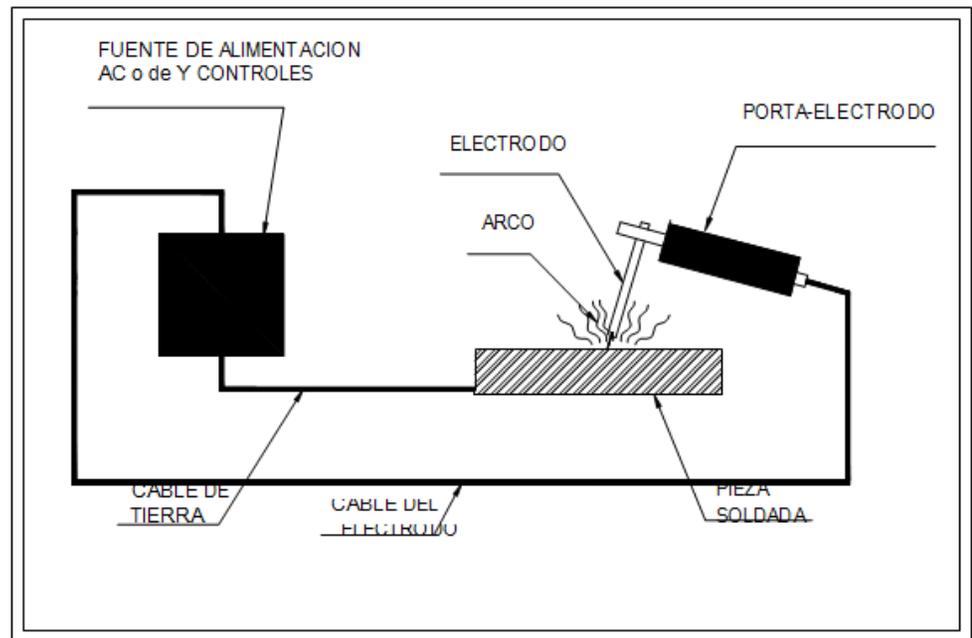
Circuito Eléctrico del proceso de soldadura al arco con electrodo revestido.
